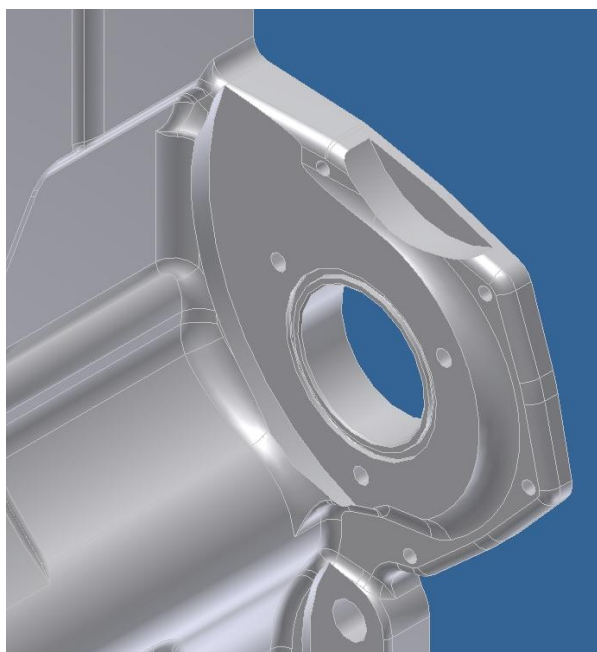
4 Prototypové čerpadlo Motorpal M3
